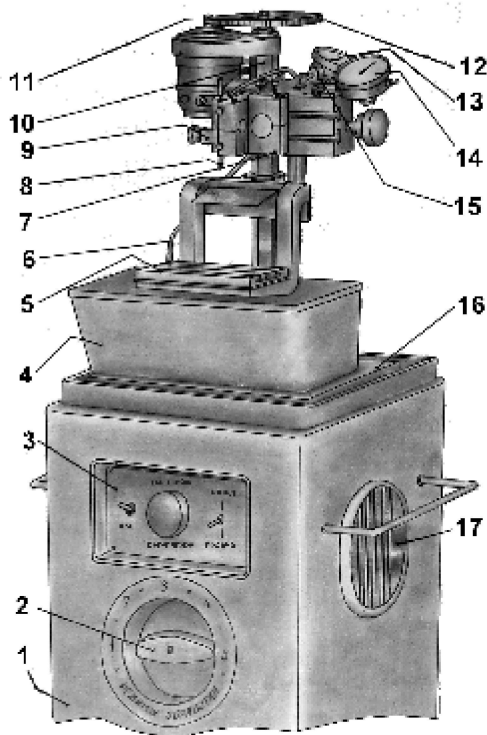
Общий вид станка: 1 – корпус; 2 – рукоятка переключателя режимов; 3 – щиток управления; 4 – ванна для рабочей жидкости; 5 – стол; 6 – провод; 7 – рабочая головка; 8 – электрод-инструмент; 9 – электрододержатель; 10 – колонка; 11 – шестерня на валу электродвигателя; 12 – зубчатое колесо на винте подачи; 13 – индикатор поперечной подачи; 14 – индикатор продольной подачи; 15 – поперечный суппорт; 16 – плита; 17 – вентиляционная решетка.
